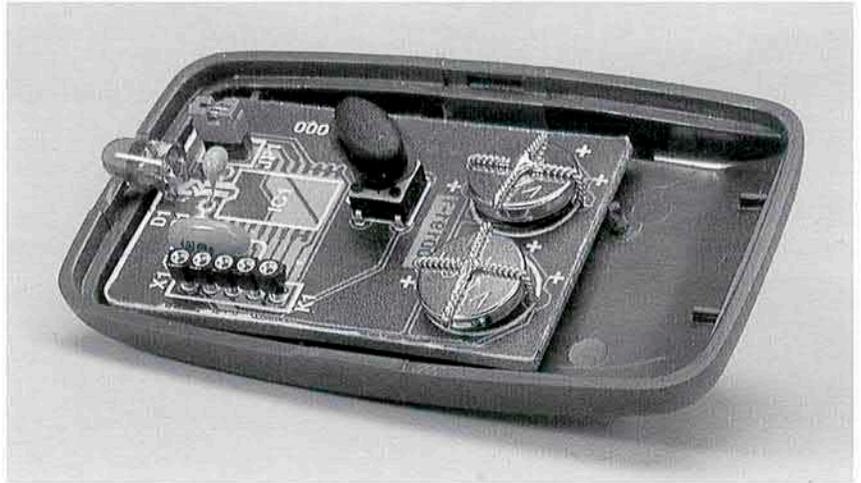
Esta pequeña caja es perfecta para la PCB del transmisor.
